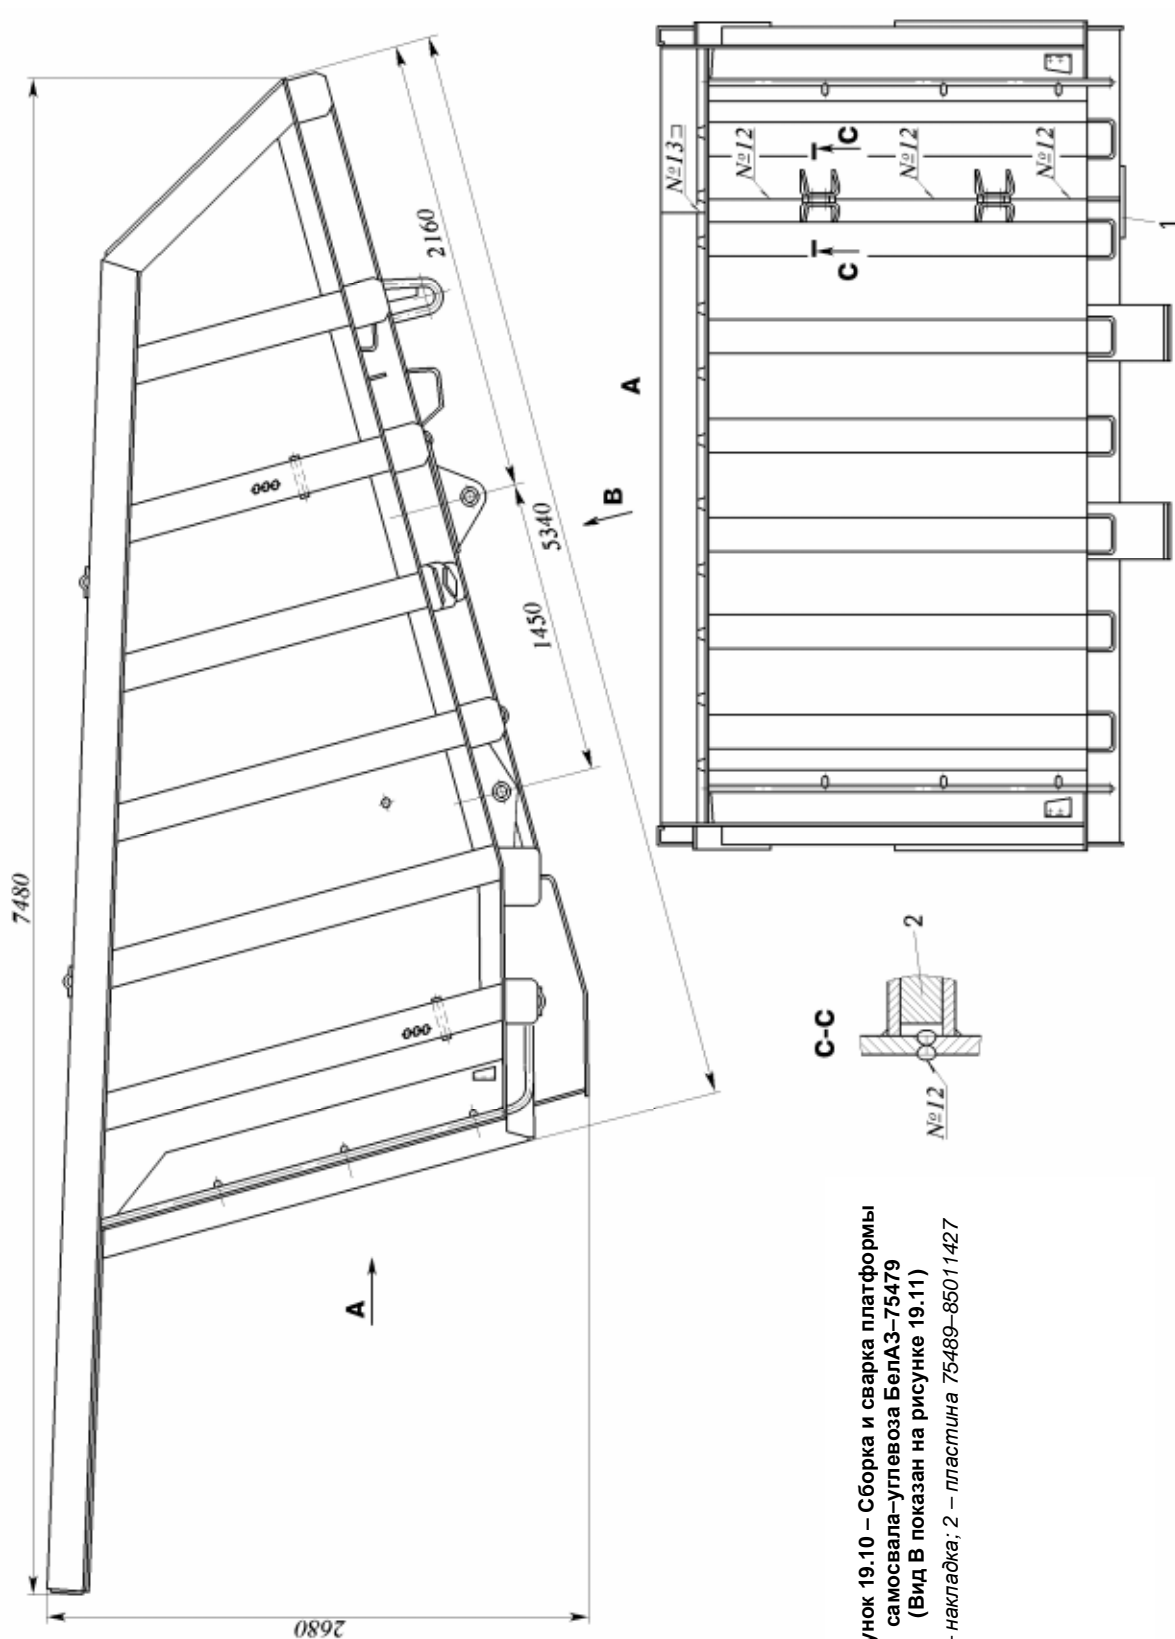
Сборка и сварка платформы самосвала-углевоза БелАЗ-75479 (Вид В показан на рисунке 19.11)
